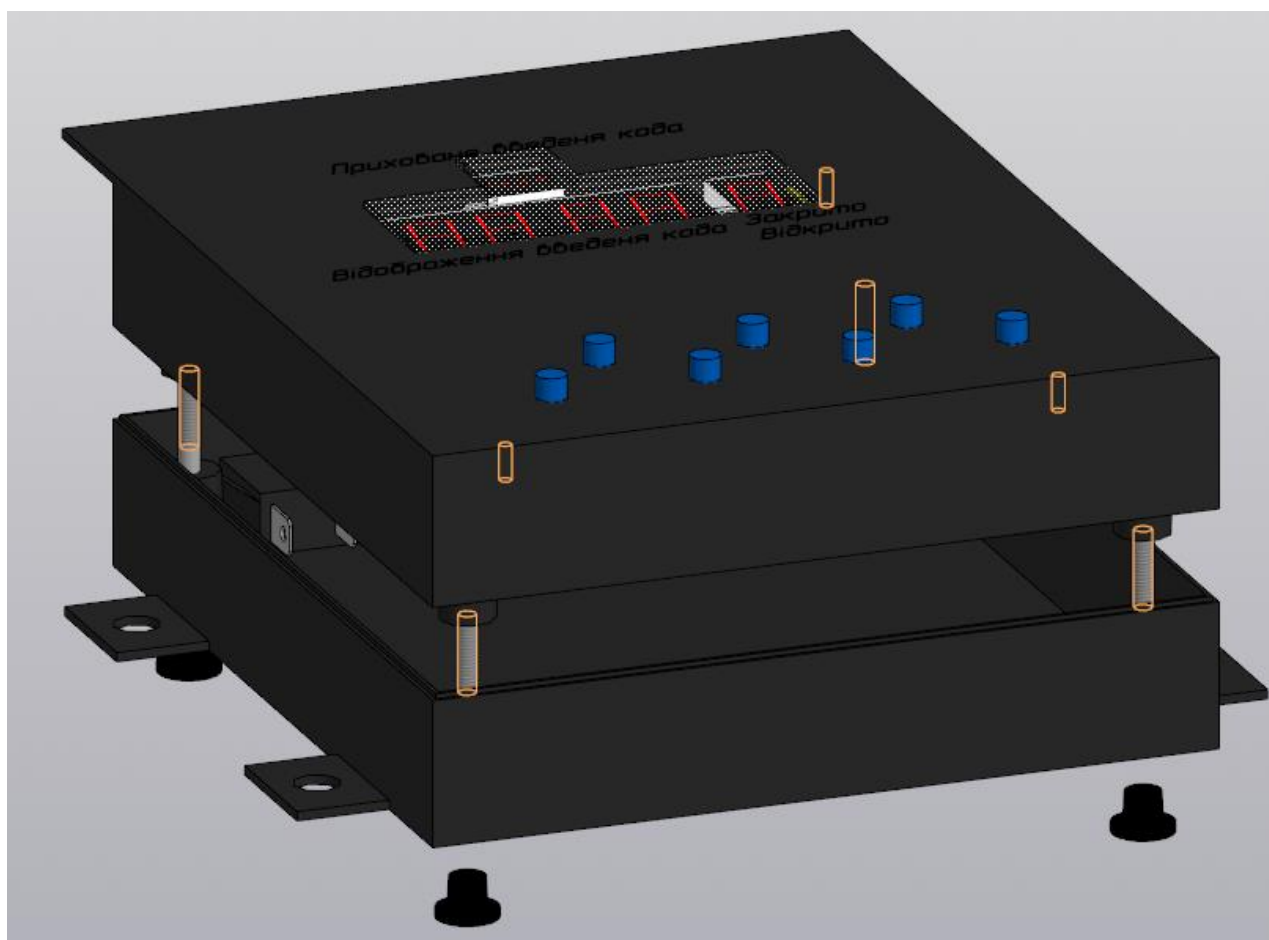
3D модель пристрою, загальний вигляд
